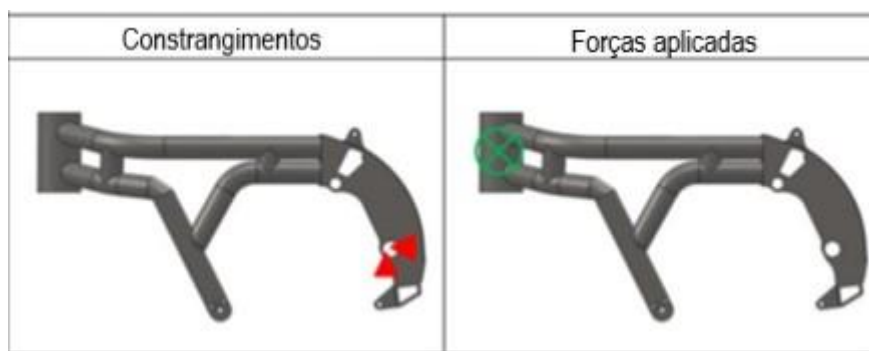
Constrangimentos e forças aplicadas (2)
